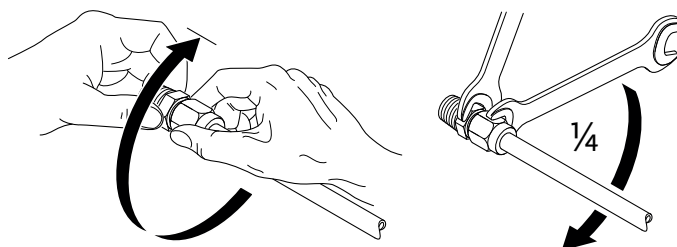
Ruotare ulteriormente il raccordo a compressione di 1/4 di giro
